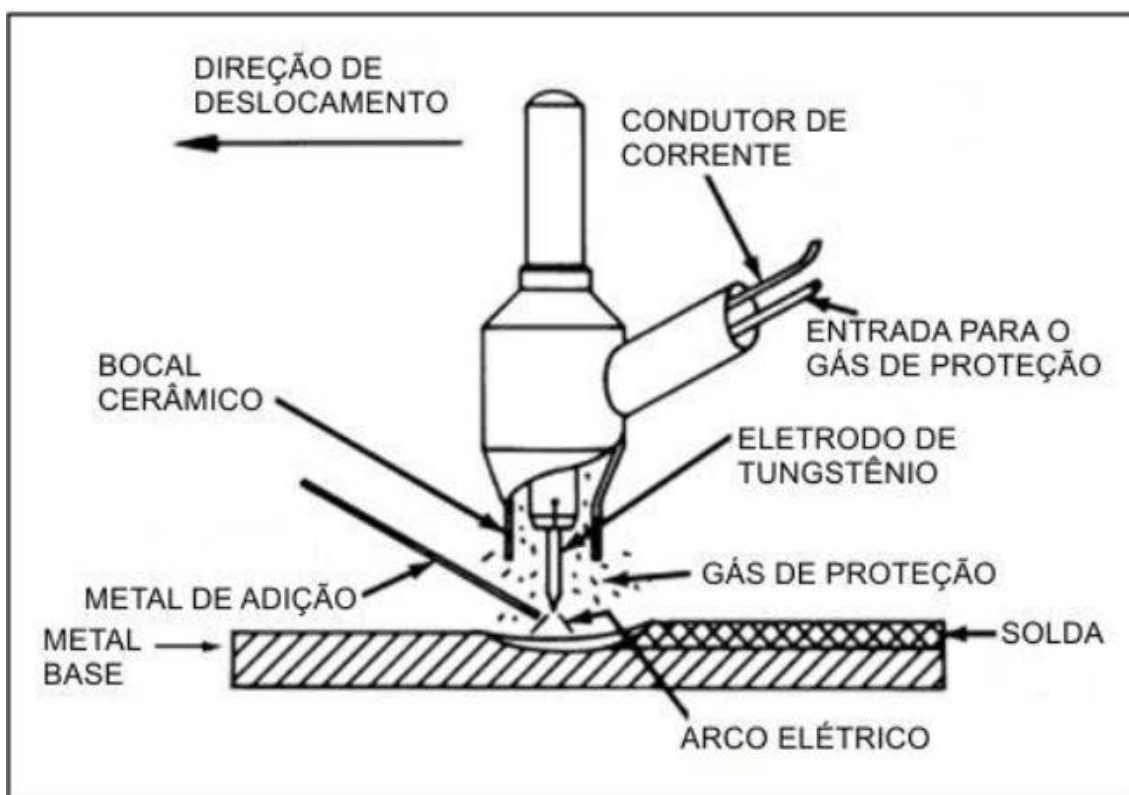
Diferentes componentes que envolvem o processo GTAW [21].
